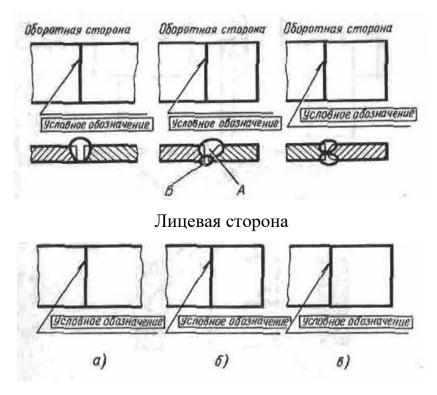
а, б, в – Изображение лицевой и оборотной стороны сварного шва
